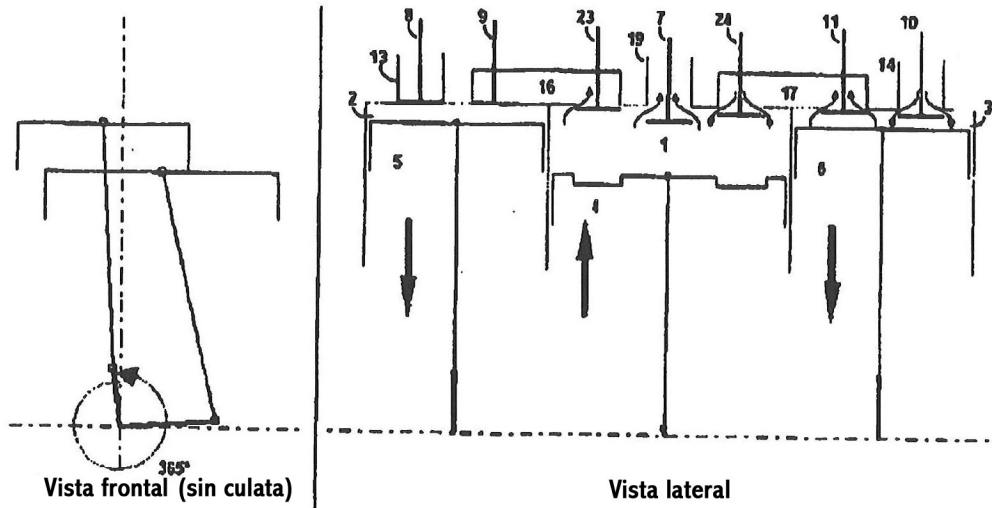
y 8a: Vistas del motor con cigüeñal a 95° después de PMH admisión cilindro de alta presión de la izquierda
